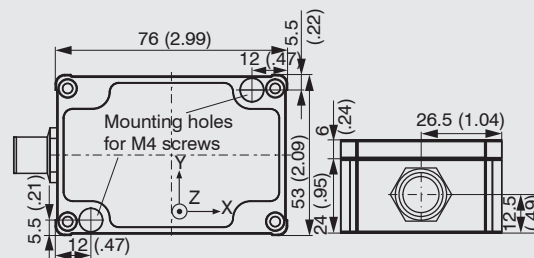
Dimensional drawing with orientation of measurement axes, dimensions in mm (inches), not to scale
